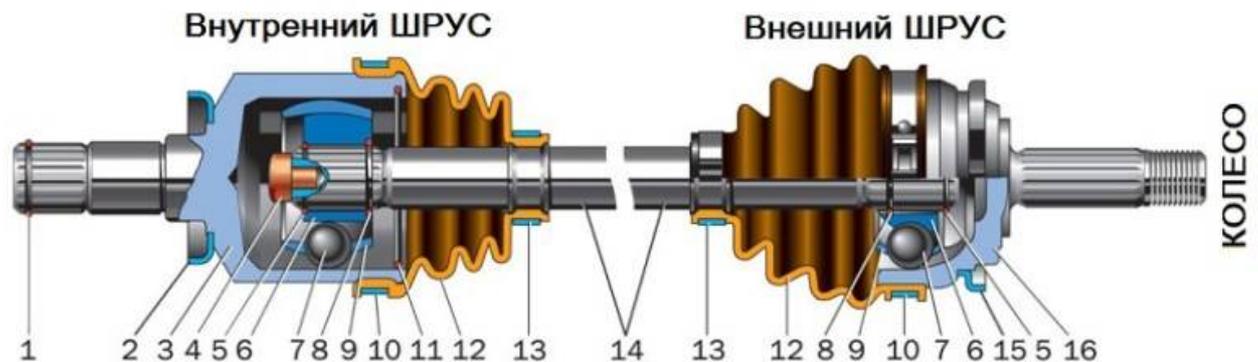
Устройство внешнего и внутреннего ШРУСа: 1 — стопорное кольцо корпуса внутреннего шарнира; 2 — защитное кольцо внутреннего шарнира; 3 — корпус внутреннего шарнира; 4 — упор вала; 5 — стопорное кольцо; 6 — обойма; 7 — шарик; 8 — упорное кольцо; 9 — сепаратор; 10 — наружный хомут; 11 — фиксатор внутреннего шарнира; 12 — защитный чехол; 13 — внутренний хомут; 14 — вал привода колеса (полуось); 15 — защитное кольцо наружного шарнира; 16 — корпус наружного шарнира.
